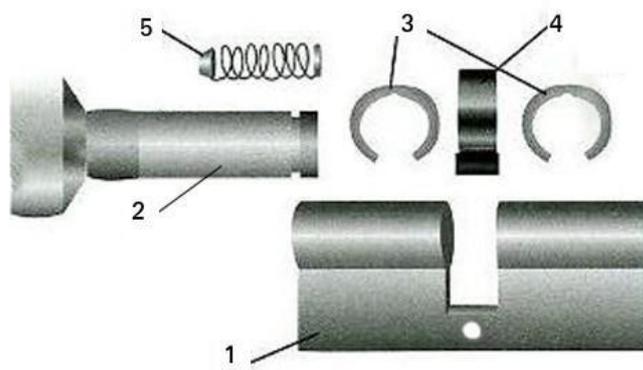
Устройство «Цилиндр замка», где: 1. Корпус. 2. Шток с ручкой (постоянный ключ). 3. Стопорное кольцо (служит для фиксации детали). 4. Кулачок (основной элемент, выполняющий вращение и вывод засова). 5. Пружина поворотной ручки.
